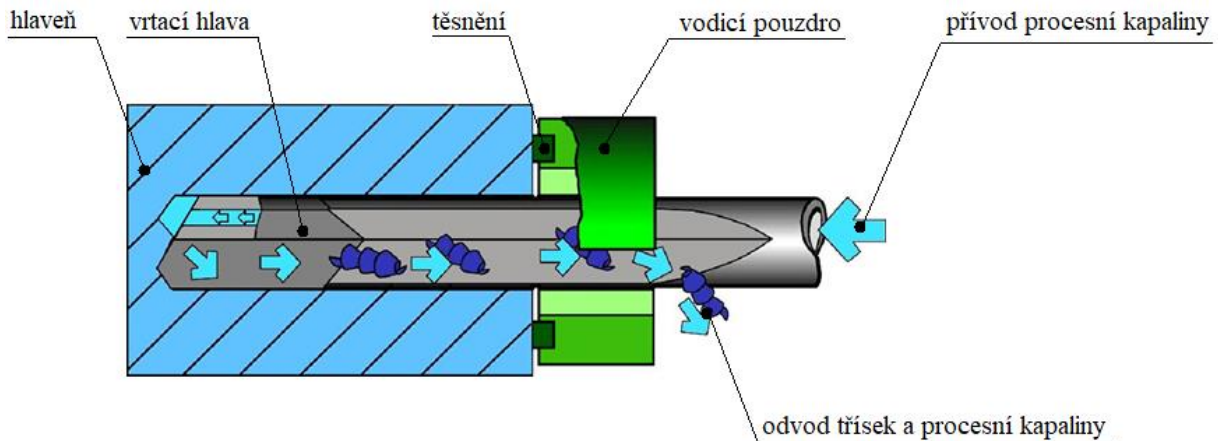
Geometrie hlavňového vrtáku – podle [16].
